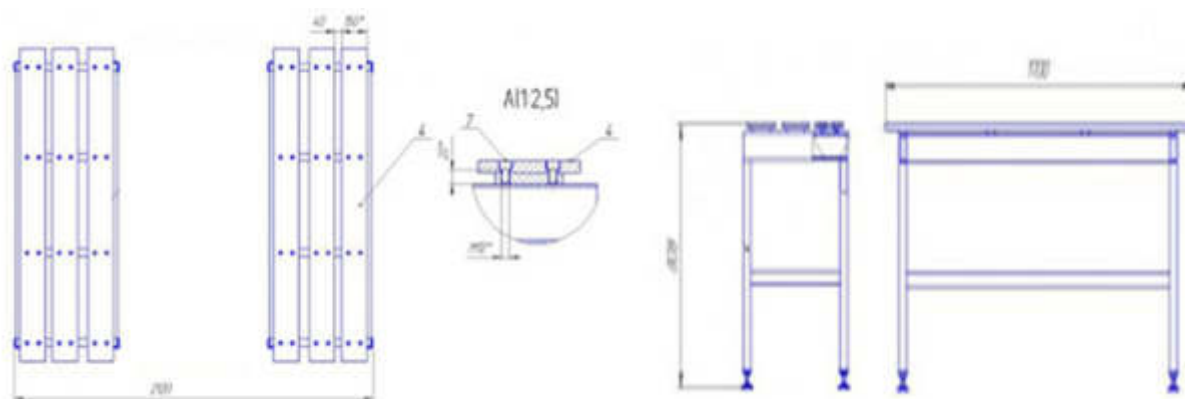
а – Сборочно-сварочный стенд.
